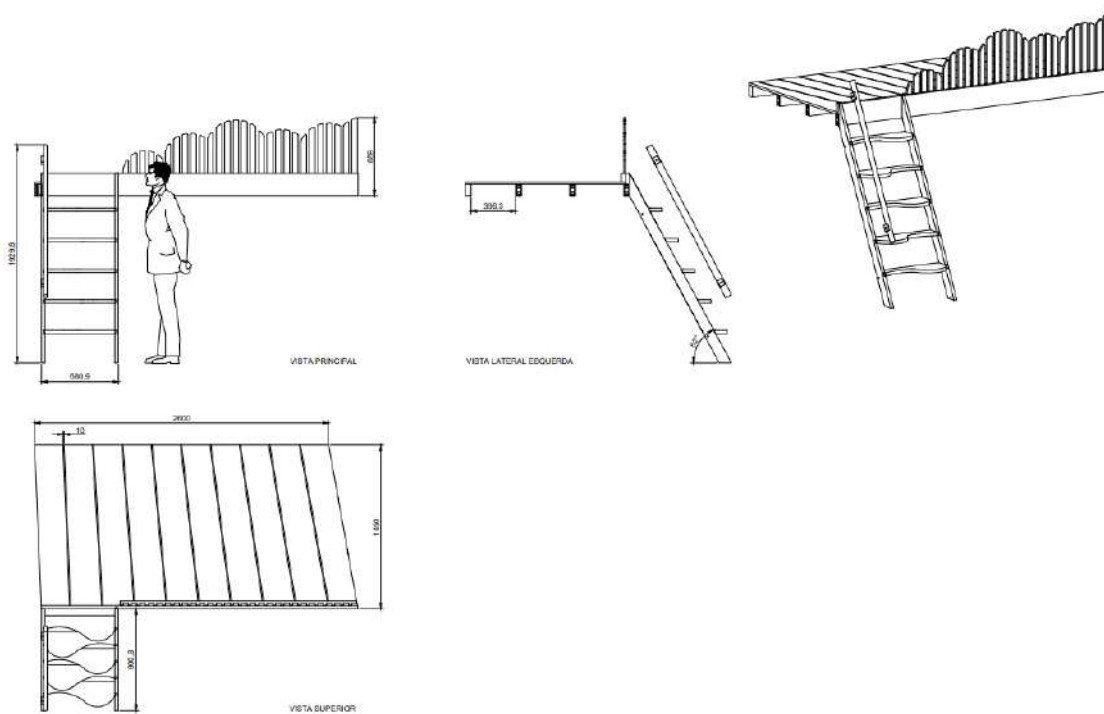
Desenho Técnico de Conjunto. Fonte: Autor
